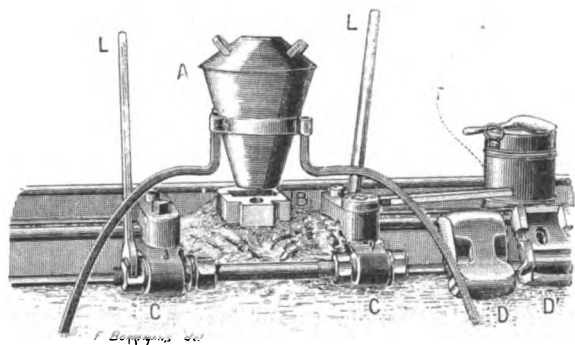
Soudure de rails (matériaux et outils nécessaires pour l'opération). — A. Creuset automatique ; B. moule mis en place ; C. appareil de serrage ; D et D', moules non utilisés ; T. boîte de thermité ; LL, leviers de l'appareil de serrage.
